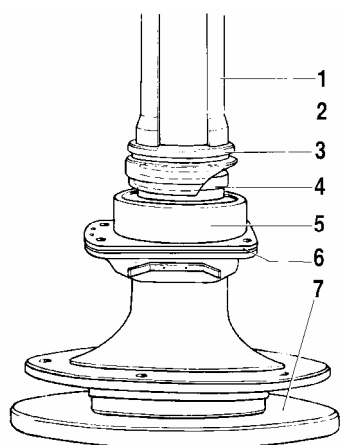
Запрессовка запорного кольца подшипника полуоси:
